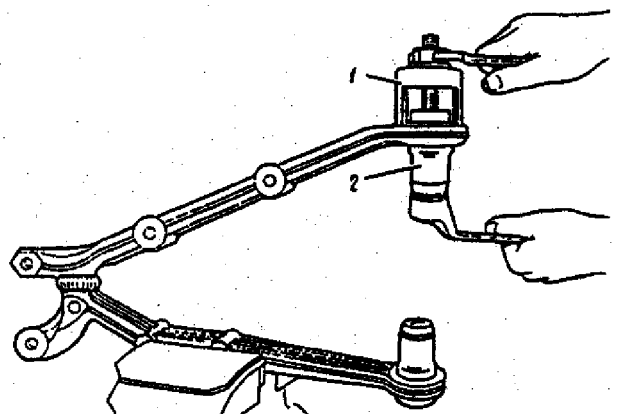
Remoção da bucha isoladora do braço inferior: 1 - dispositivo 67.7823-9517; 2 - bucha isoladora.
